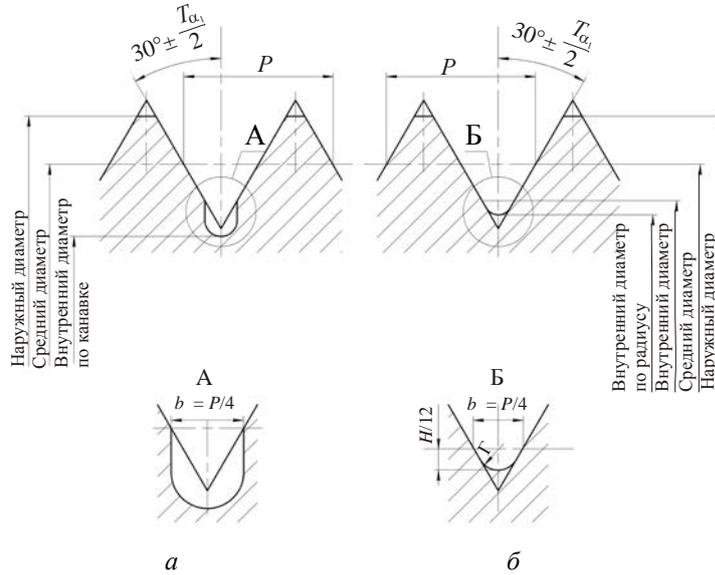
Полный профиль резьбы калибров-пробок для метрической резьбы:
